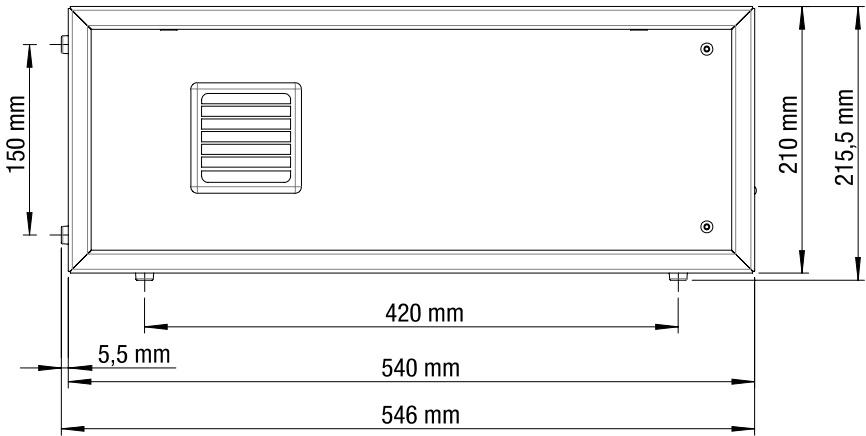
Seitenansicht – Steuerung G-FRAME 54 (exemplarisch)
